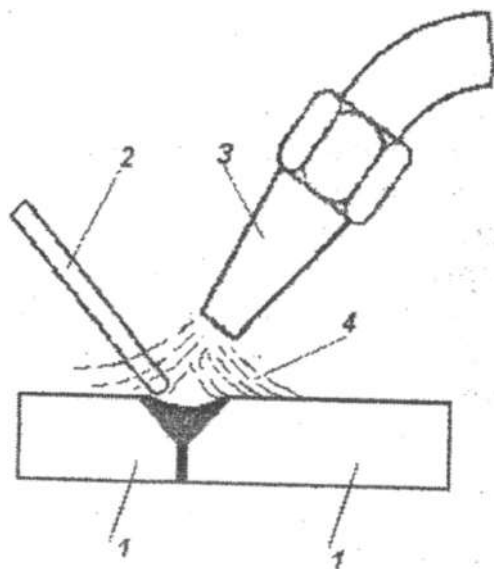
Схема газовой сварки армированной шамотной плиткой
